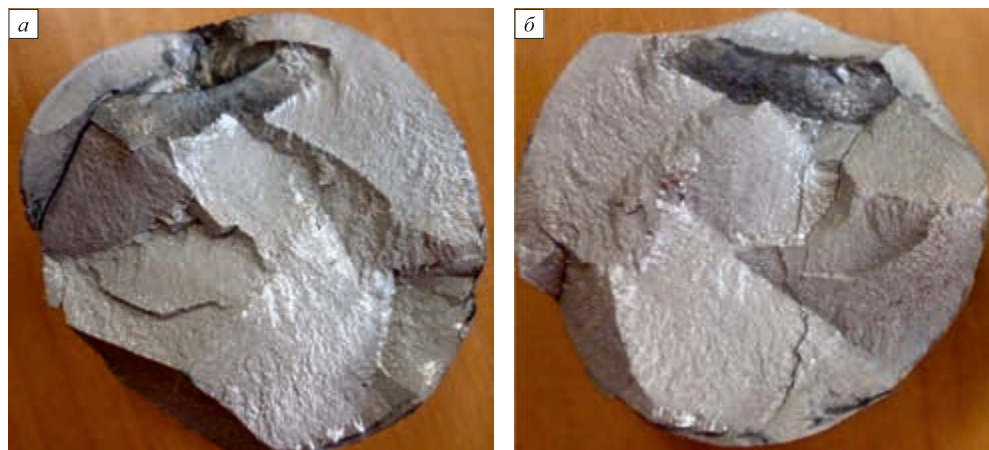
Общий вид изломов шаров, прокатанных из заготовок без дефектов макроструктуры
